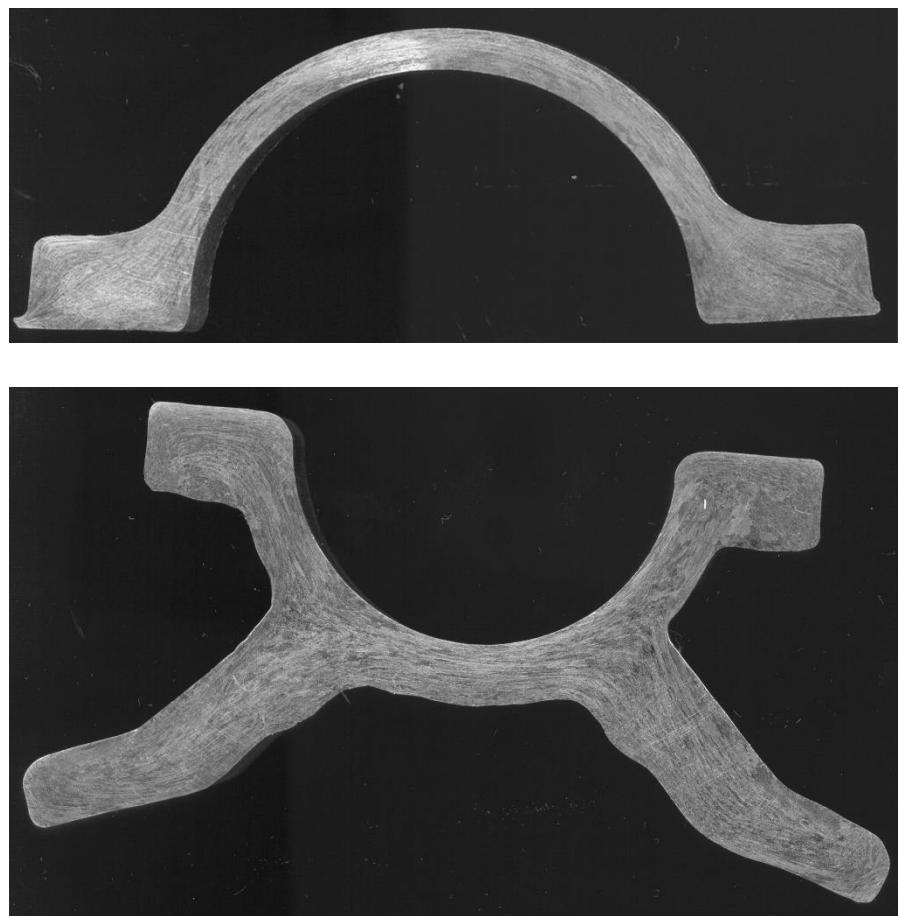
Макроструктура штампованных поковок. (Верхняя фотография деталь «Крышка», нижняя фотография – деталь «Основание» для сборочного узла «Корпус»).
